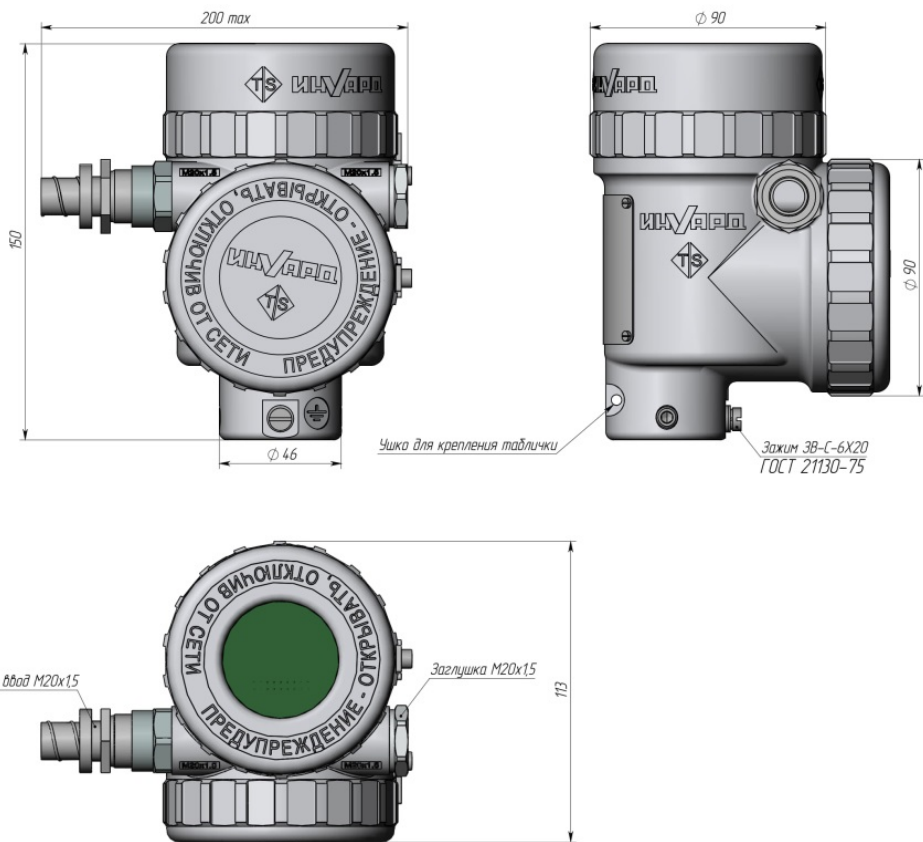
Габаритные и установочные размеры алюминиевого мини корпуса блока электронного преобразователя.Р67. Дисплей сбоку
